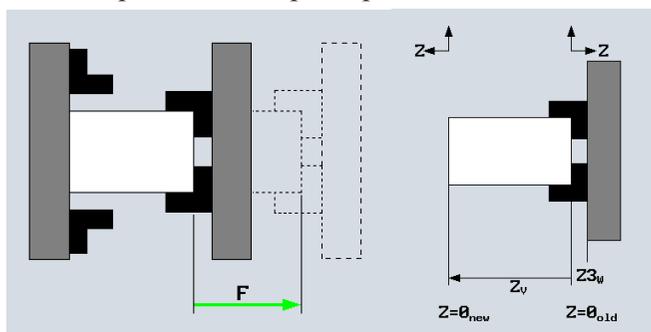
Параметры перехвата заготовки в противощпиндель
